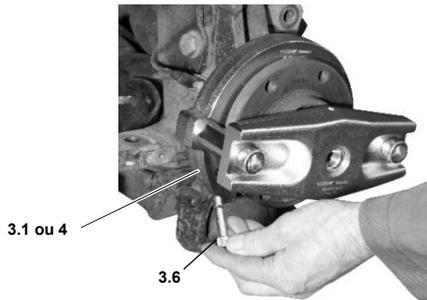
Fixer les barres d'appui sur la barre de renforcement.
